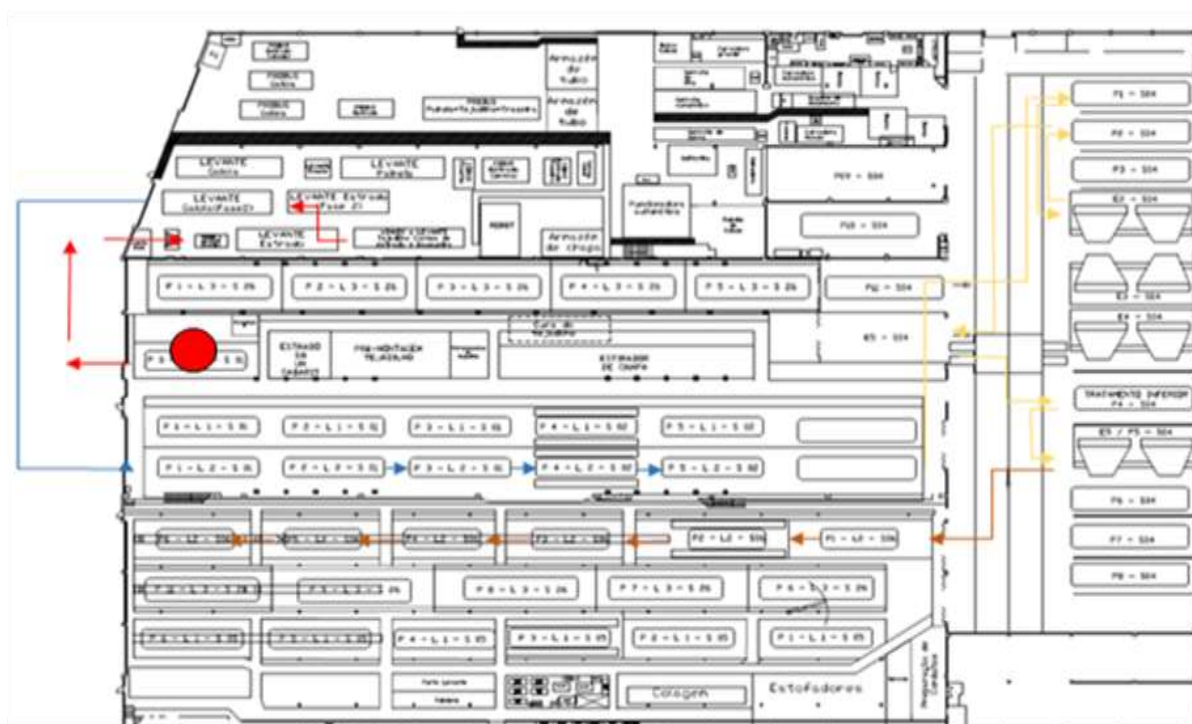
Layout da empresa e seguimento das linhas de produção
